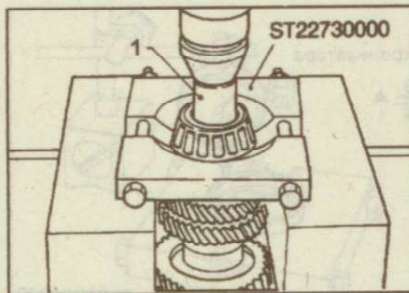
Использование пресса и оправки (1) для снятия заднего подшипника вторичного вала
